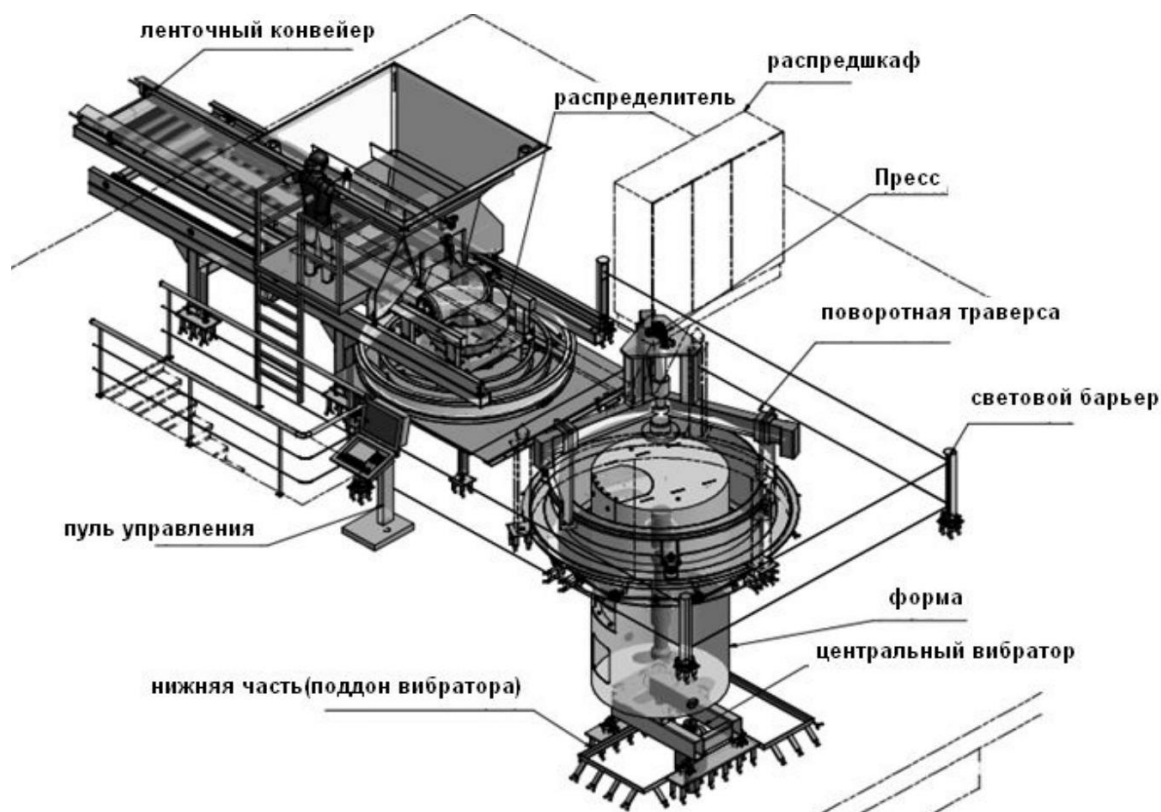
Общая схема установки вибропрессования Atlas немецкой компании PRINZING PFEIFFER
